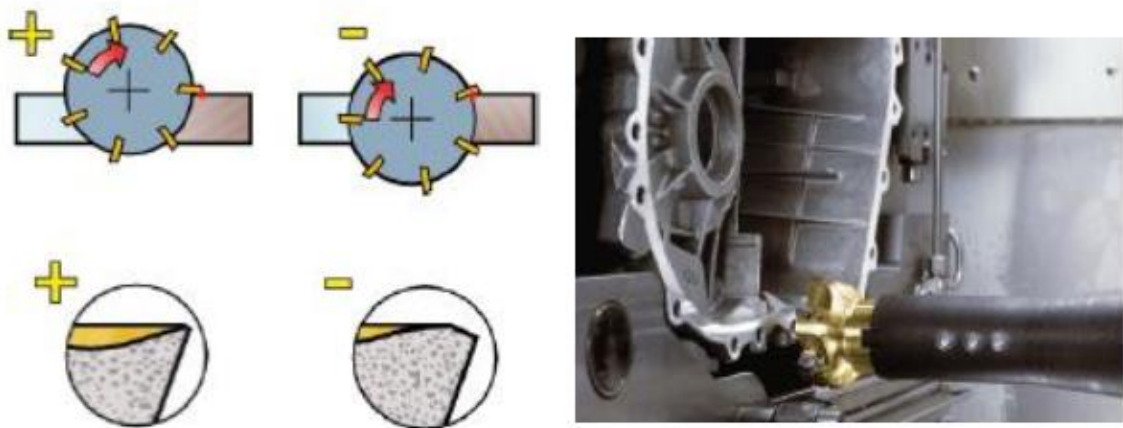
Обробка кромek тонкостінних деталей торцевими фрезами [1]
